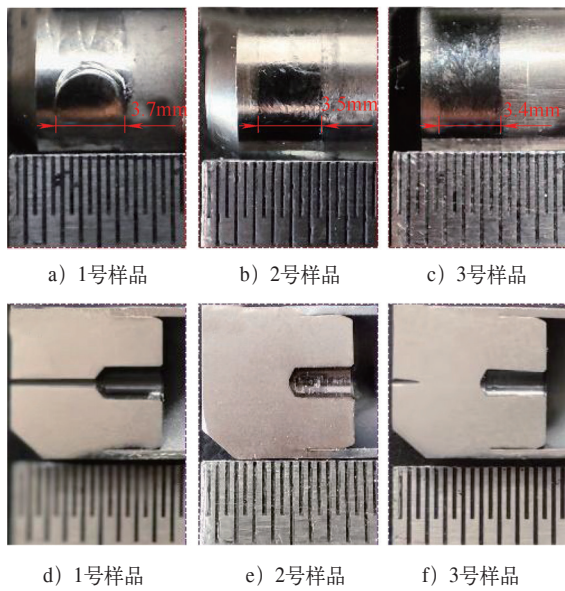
不同端面粗糙度下焊缝成形的宏观形貌
